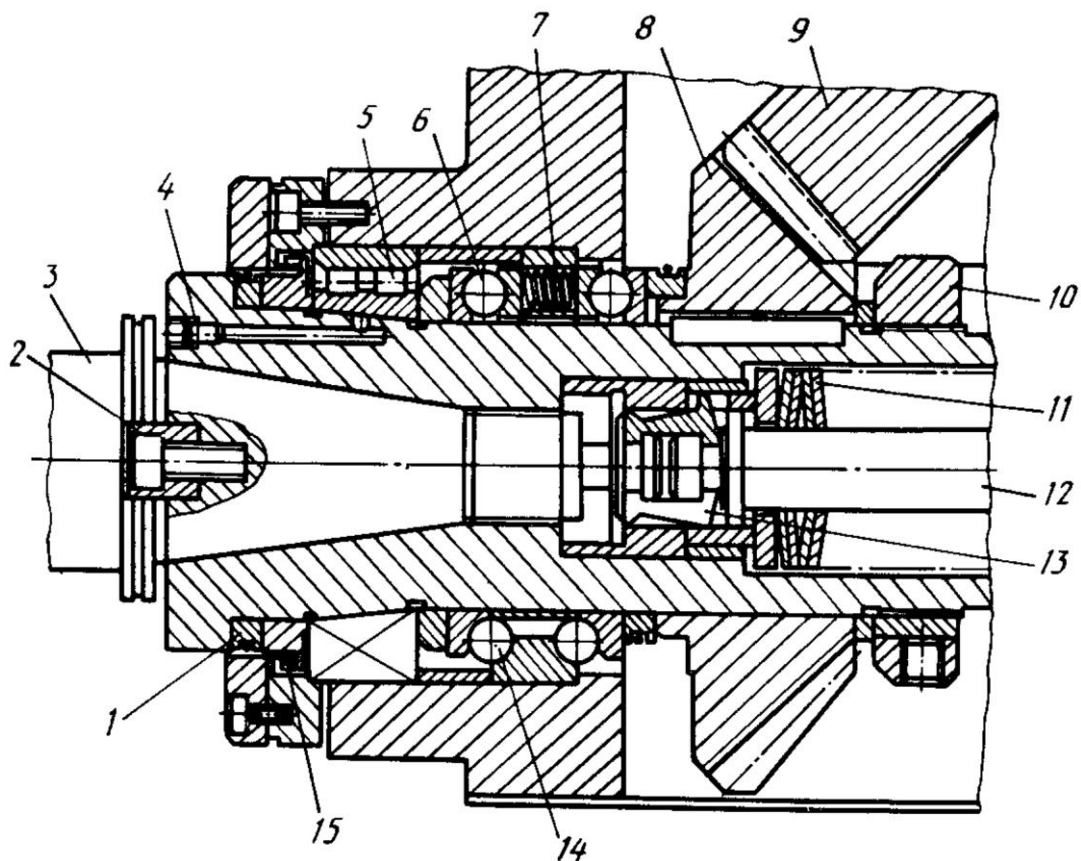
Передня опора та кінець шпинделя фрезерно-розточувального верстата з ЧПК
